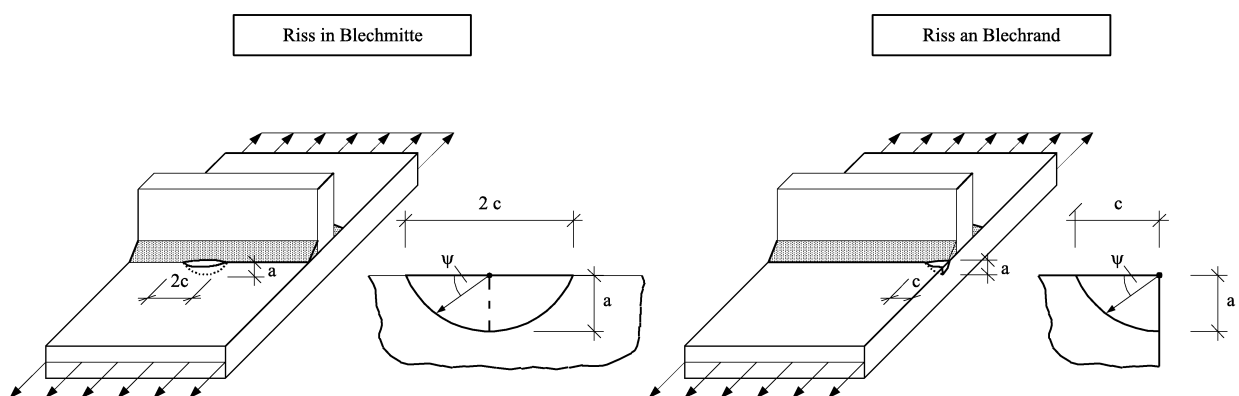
Definition der Rissgeometrie für Riss in Blechmitte und Riss am Blechrand
